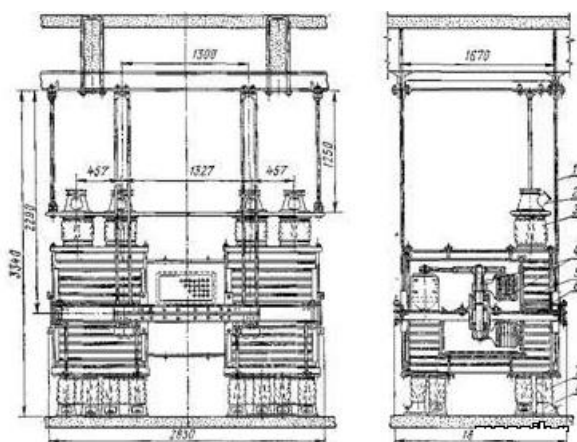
Рассев ЗРМ-2М: 1 — трос; 2 — приемная аспирационная коробка; 3 — приемный рукав; 4 — балансирный механизм; 5 — ситовой корпус; 6 — главная рама; 7 — выпускной рукав; 8 — выпускной патрубок
